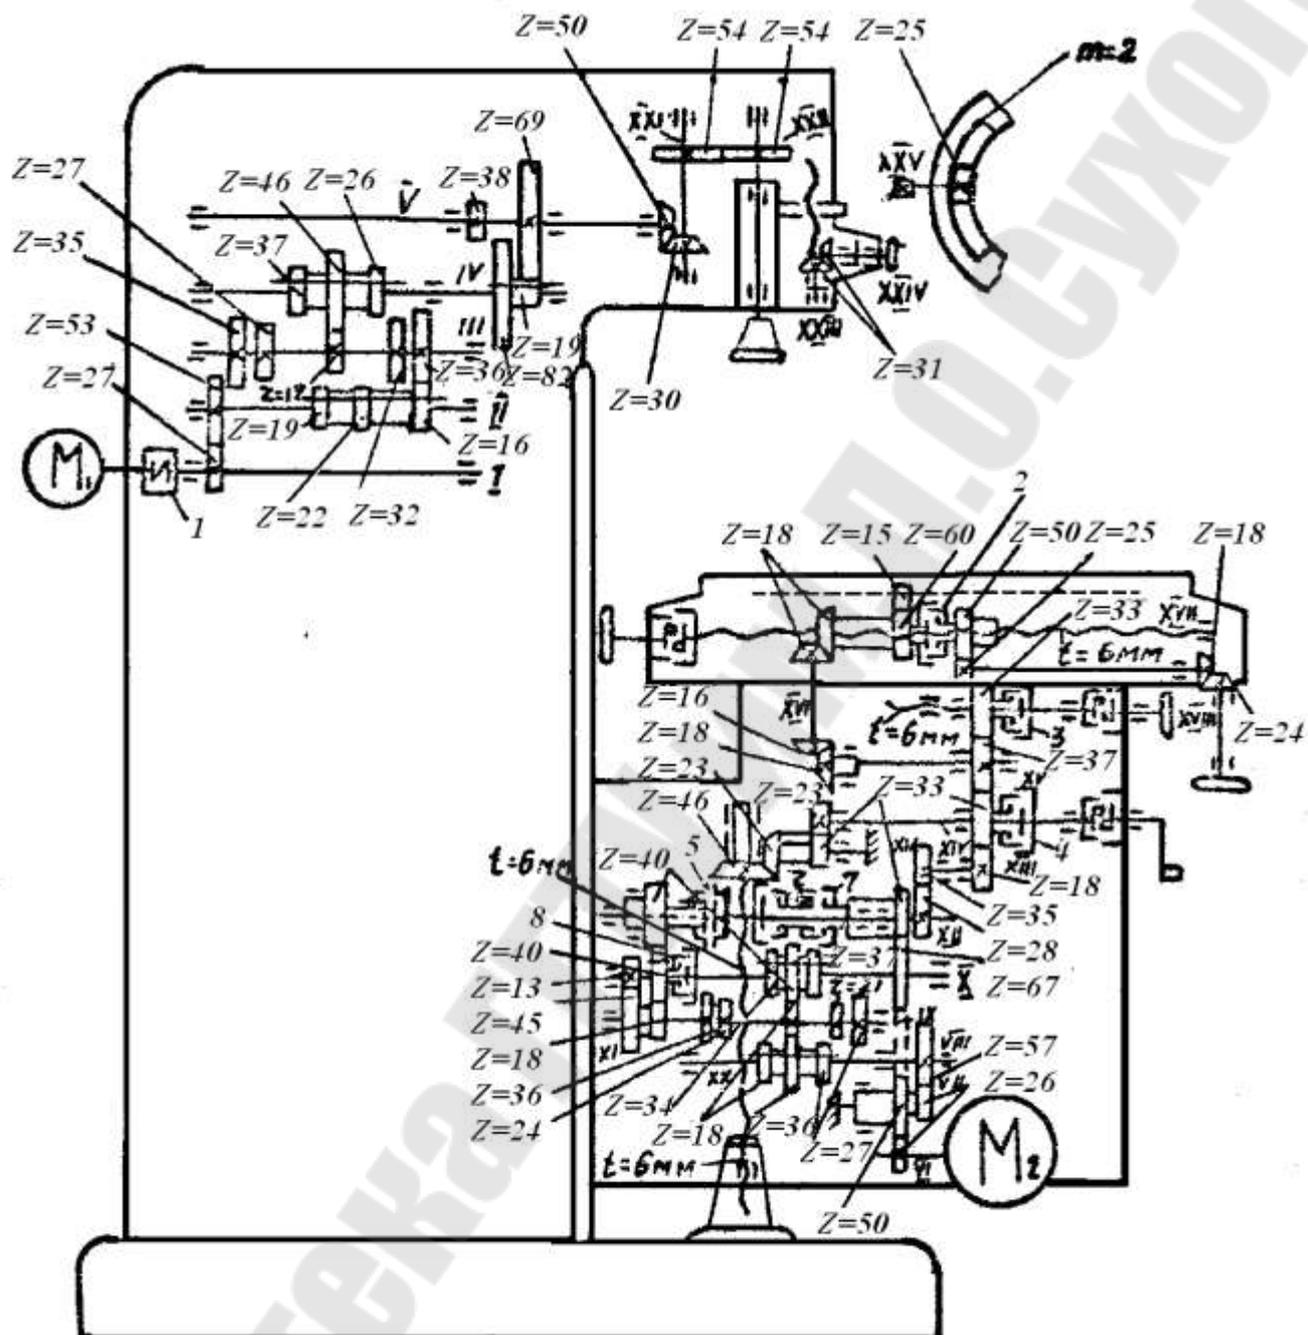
Кинематическая схема вертикально-фрезерного станка
